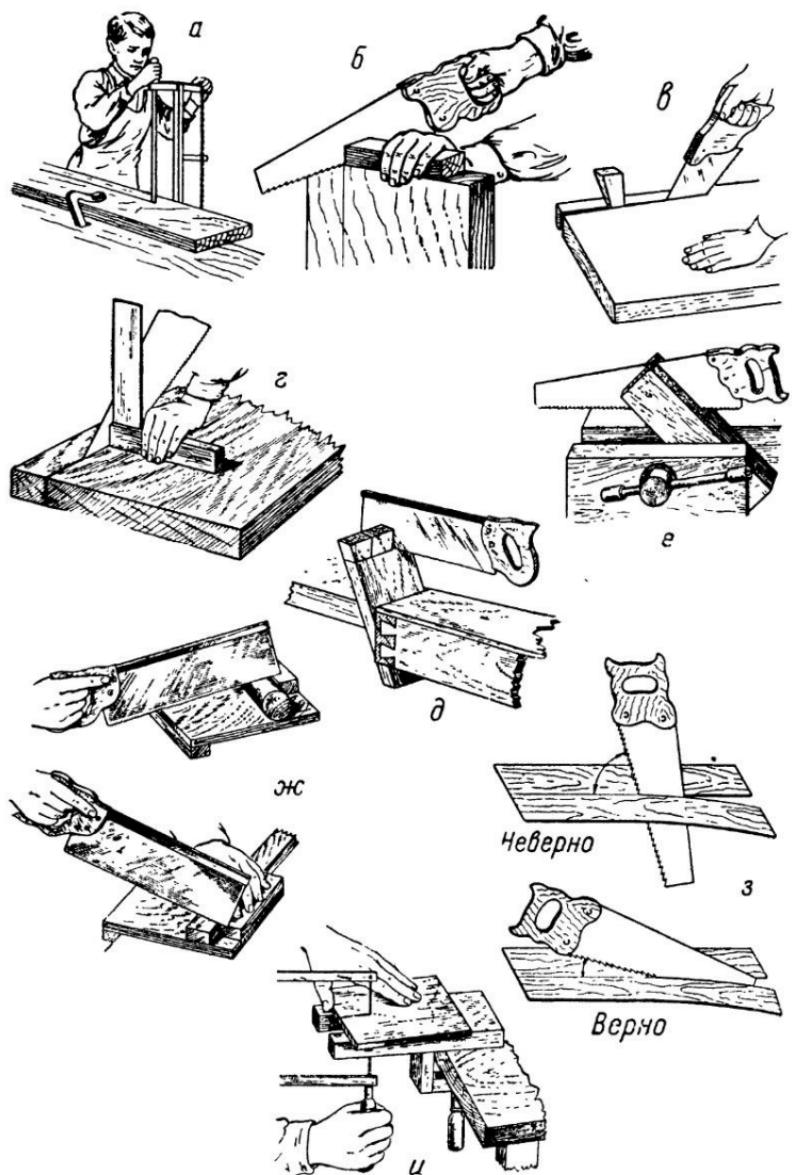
Приемы работы пилами: а — распашное пиление; б — как начинать пропил; в — расклинивание пропила; г — проверка положения полотна ножовки по угольнику; д — запиливание шипов; е — пропиливание вдоль пластин; ж — пиление с упором; з — пиление фанеры; и — выпиливание лобзиком.
